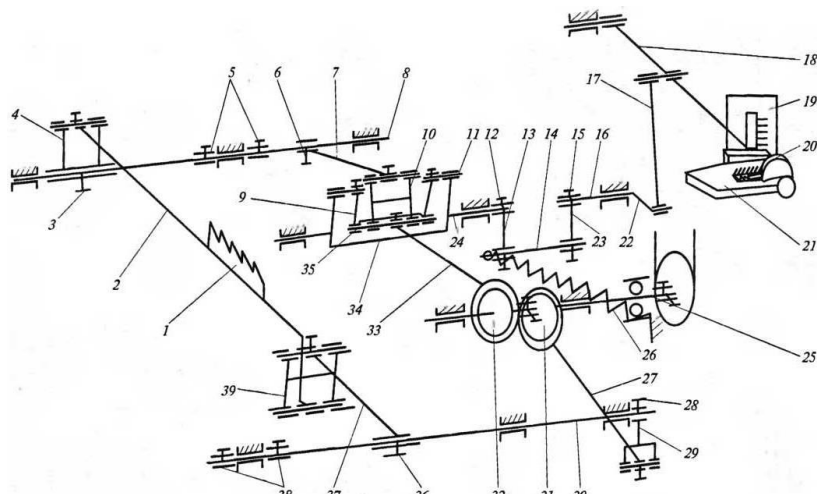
Кинематическая схема механизма перемещения рейки в швейной машине класса 31-12+3
